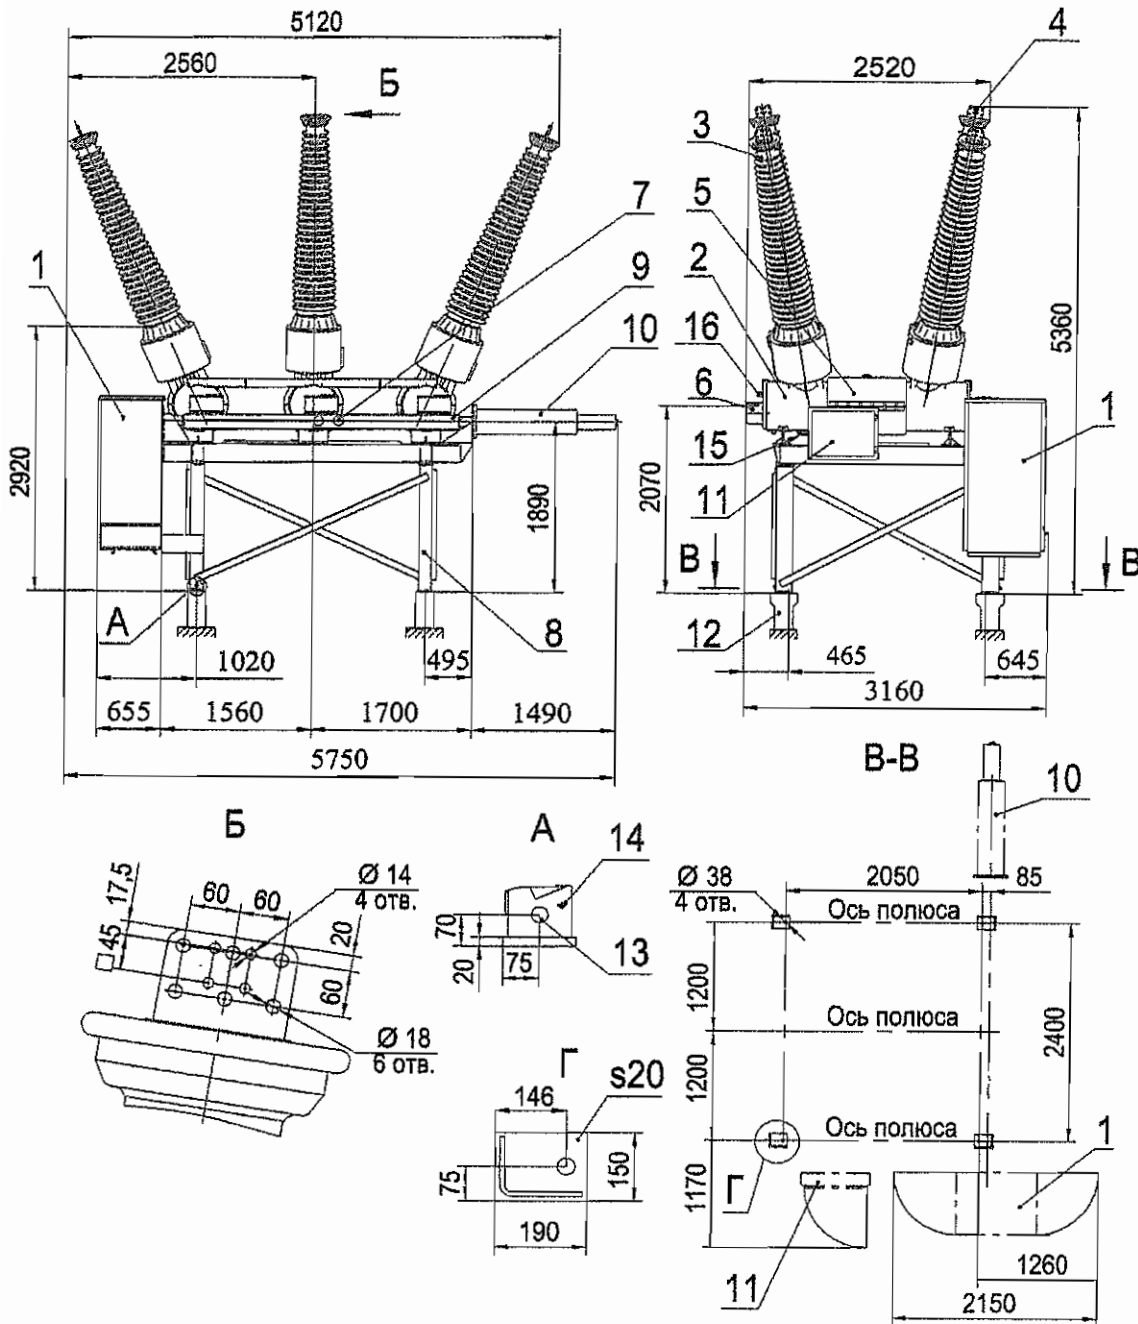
Габаритные и присоединительные размеры выключателя типа ВЭБ-220
